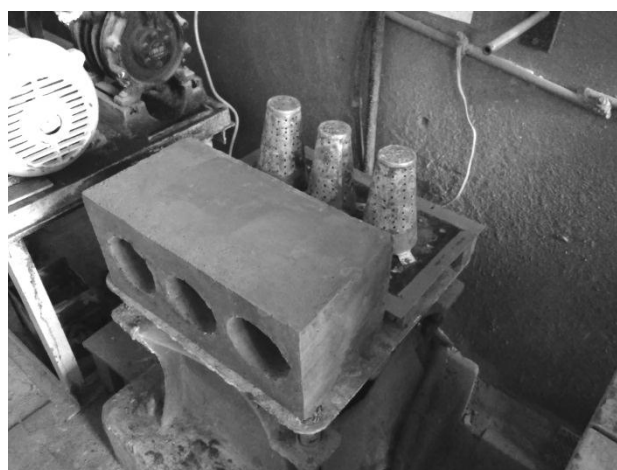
Немедленная распалубка свежесформованных виброввакуумированием золобетонных стеновых блоков
